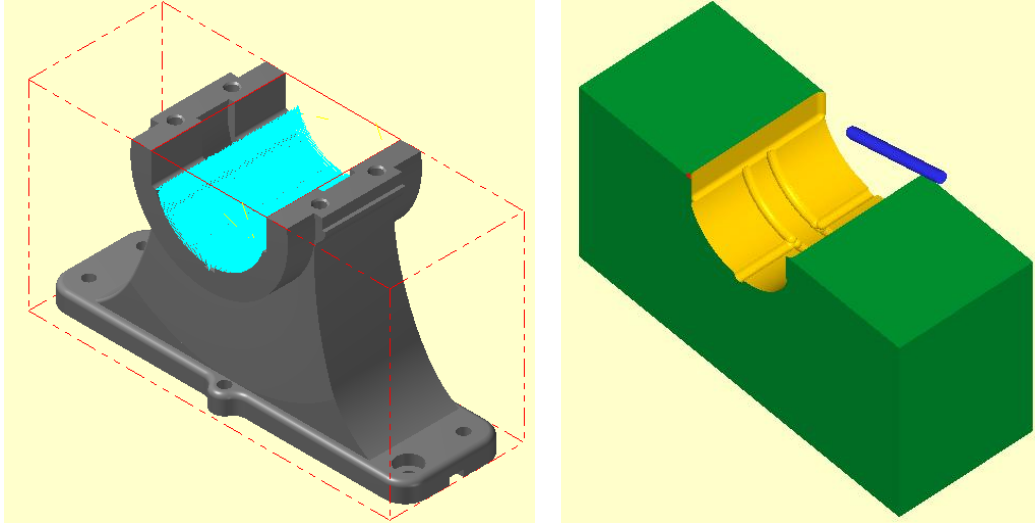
Tool Axis Control sekmesi parametre şekilleri
